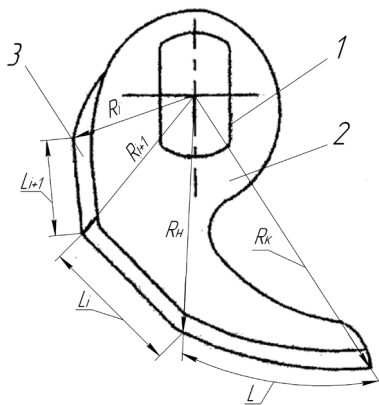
Принципиально конструктивная схема куттерного ножа с ломаной режущей кромкой, выполненной по логарифмической спирали: 1 – ступица; 2 – лезвие; 3 – режущая кромка
